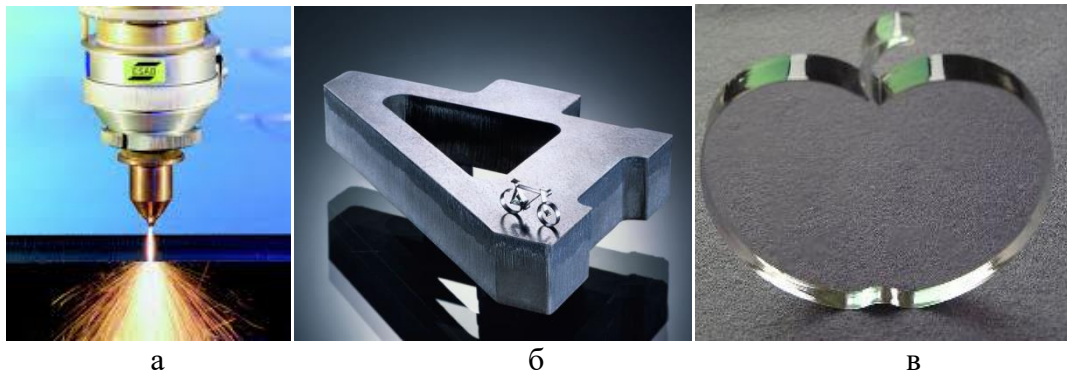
Лазерне різання: а) лазерний різак; б) розкрій металу; в) різання пластику
